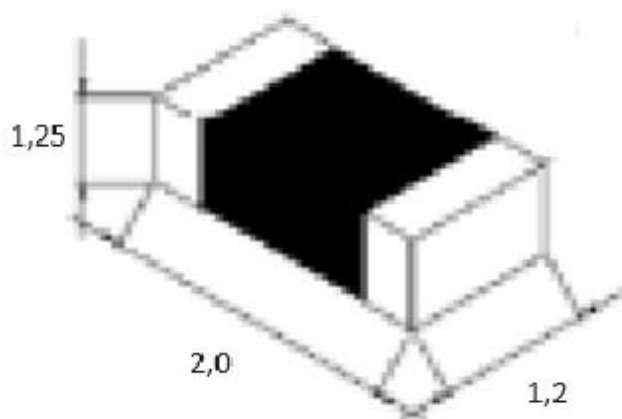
Зовнішній вигляд та габаритні розміри дроселя в корпусі SMI0805
